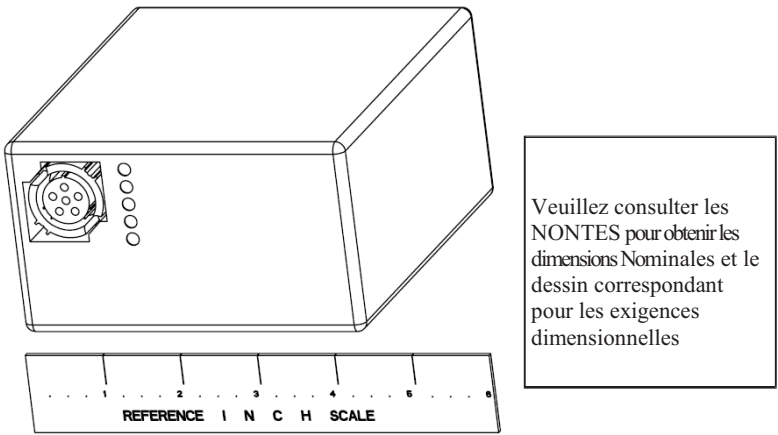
Vue d'ensemble, forme de la batterie M32271/
